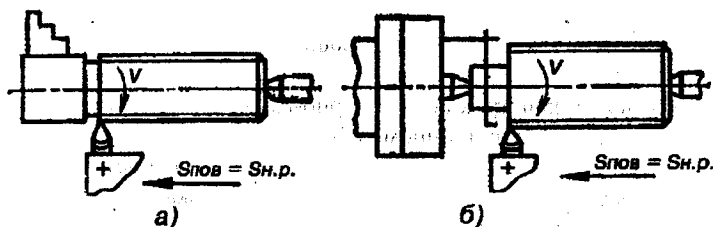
Схеми нарізування однозаходної та багатозаходної різі на токарно-гвинторізному верстаті
